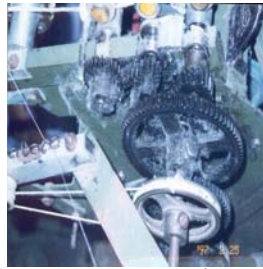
เครื่อง Roving machine ขนาดเล็กเพื่อผลิต Sliver สำหรับปั่นด้ายแบบ Ring spinning machine ด้วยมือ
